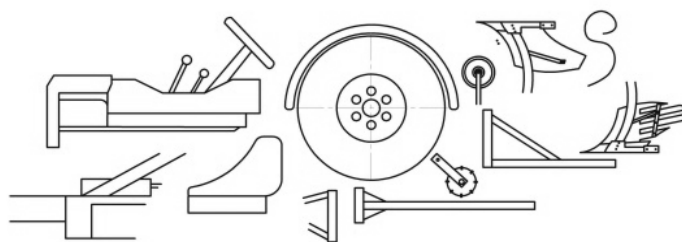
Пахотный агрегат на базе мини-трактора
